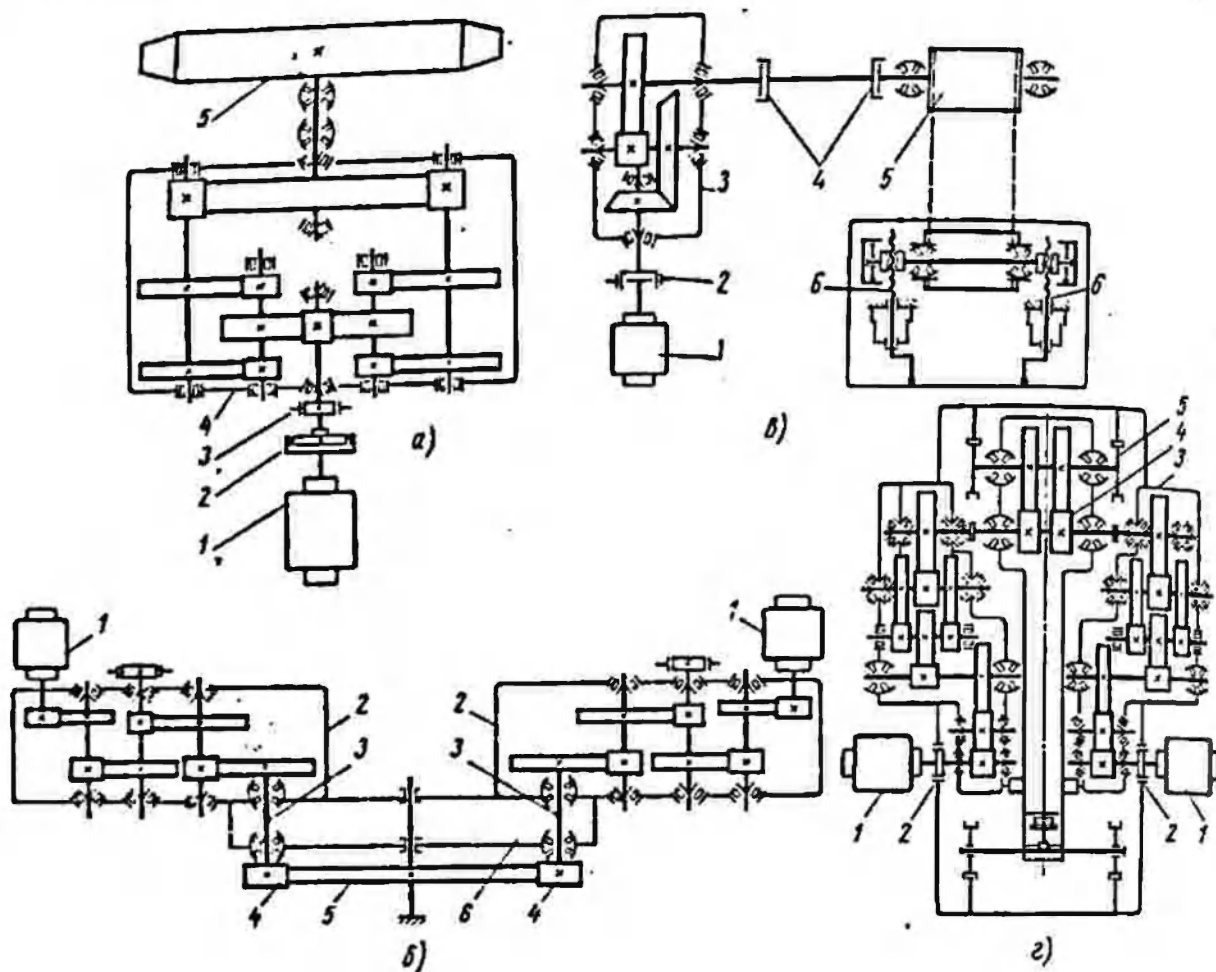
Кинематические схемы основных механизмов привода роторного экскаватора ЭРГ-400 $\frac{17}{1,5}$:
